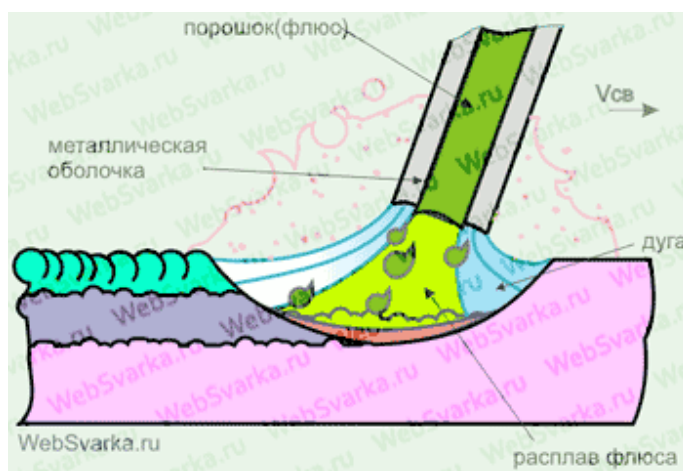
Схема выполнения наплавки порошковой проволокой
